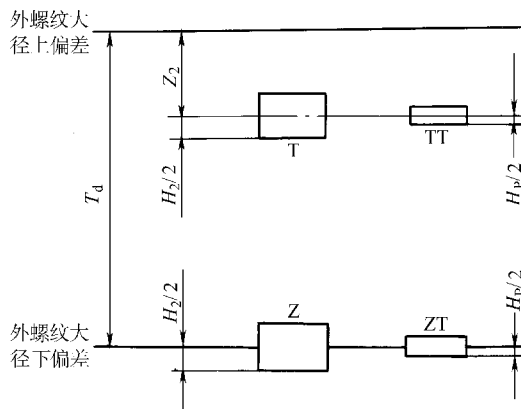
检验工件外螺纹大径用的光滑极限量规尺寸公差带图
